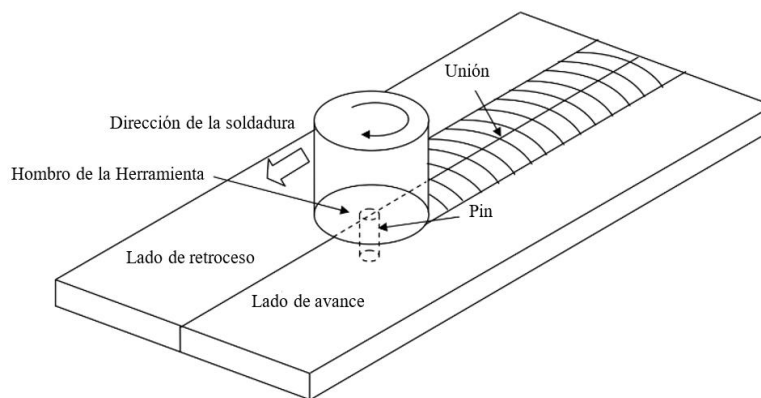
Esquema de soldadura por fricción agitación [11].
